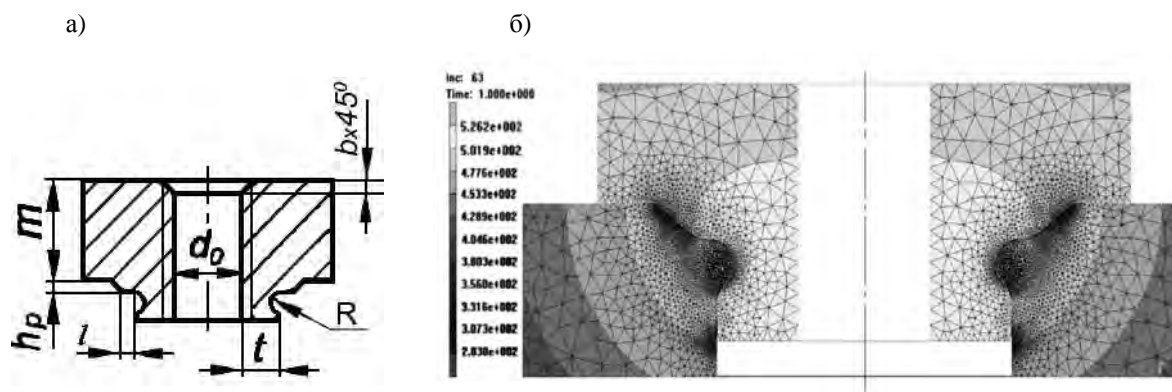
Рельеф для сварки «острой гранью»: а – конструктивные размеры; б – характер пластического деформирования металла зоны сварного соединения (данные математического моделирования)
